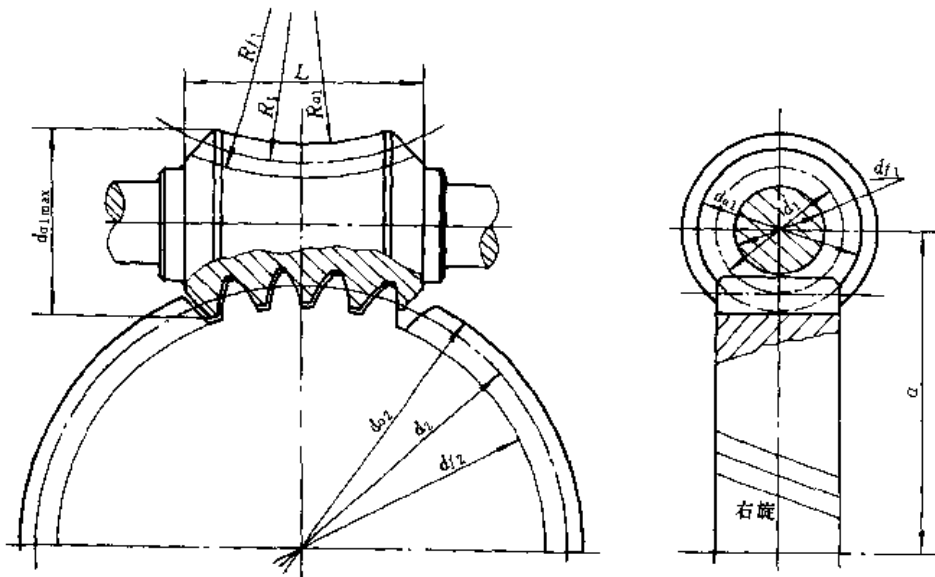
渐开线圆柱齿轮-环面蜗杆传动几何尺寸
